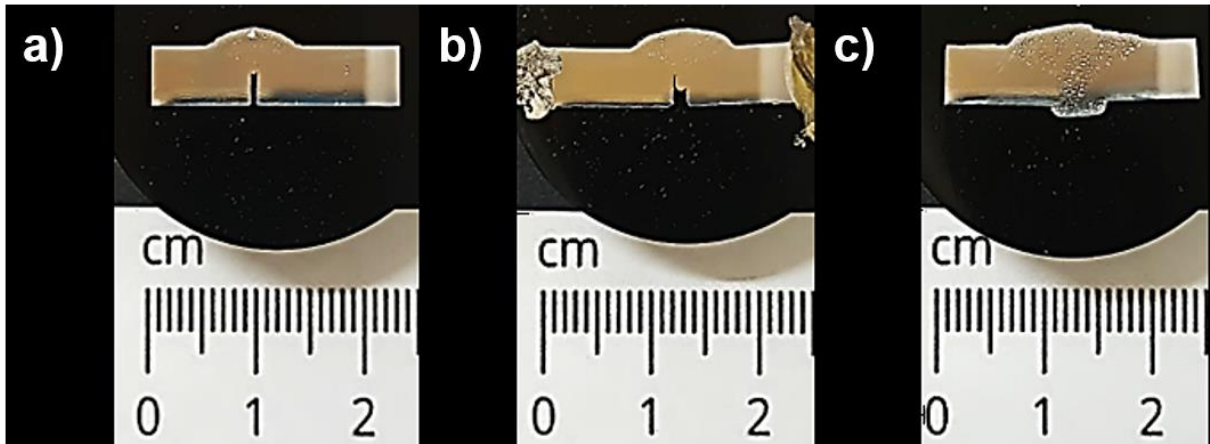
1 Soldaduras por el proceso GMAW semiautomatizado en donde a) soldadura 5, b) soldadura 7 y c) soldadura 8.
